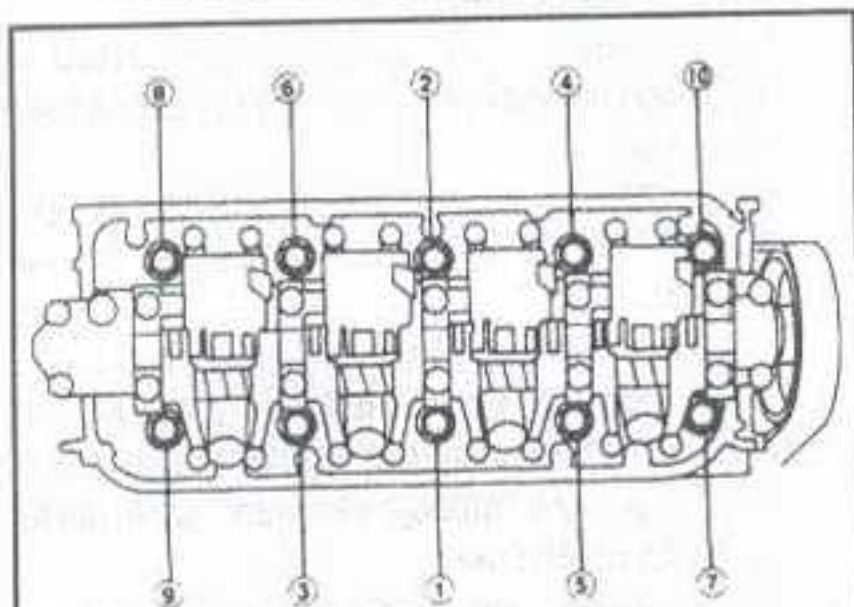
Порядок затяжки болтов головки цилиндров — все четырехцилиндровые двигатели
